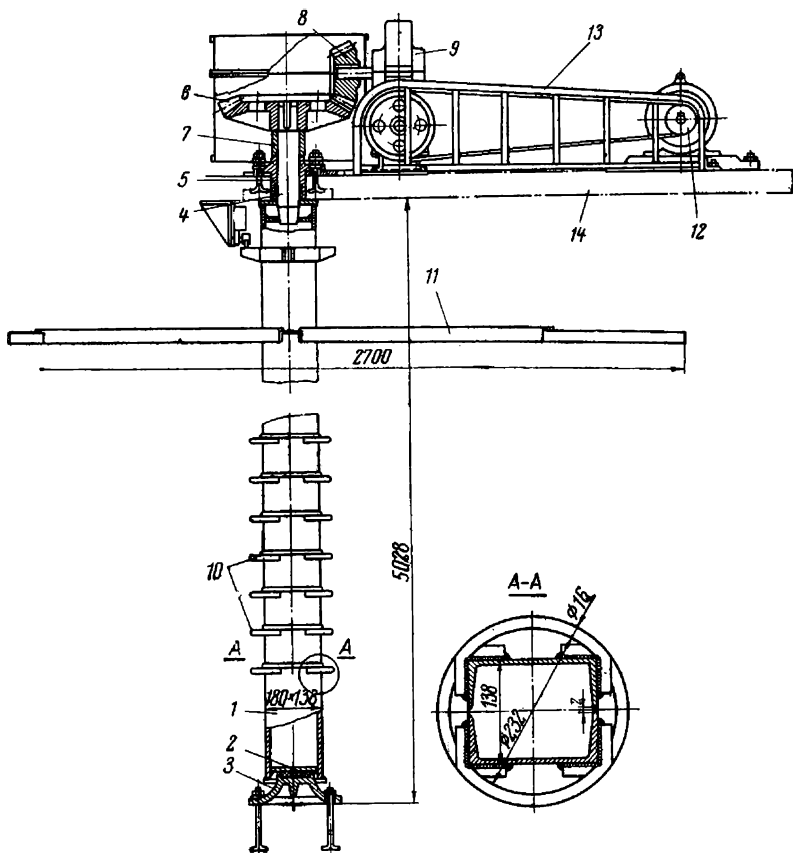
Поворотный фиксатор к агрегату для съемки шкур с туш крупного рогатого скота
